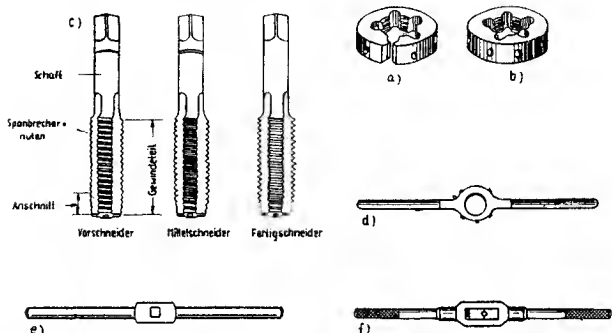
Gewindeschneidwerkzeuge; offenes Schneideisen (a), geschlossenes Schneideisen (b), ein kompletter Satz Gewindebohrer (c), Schneideisenhalter (d), Einlochwindeisen (e) und verstellbares Windeisen (f) für Gewindebohrer
